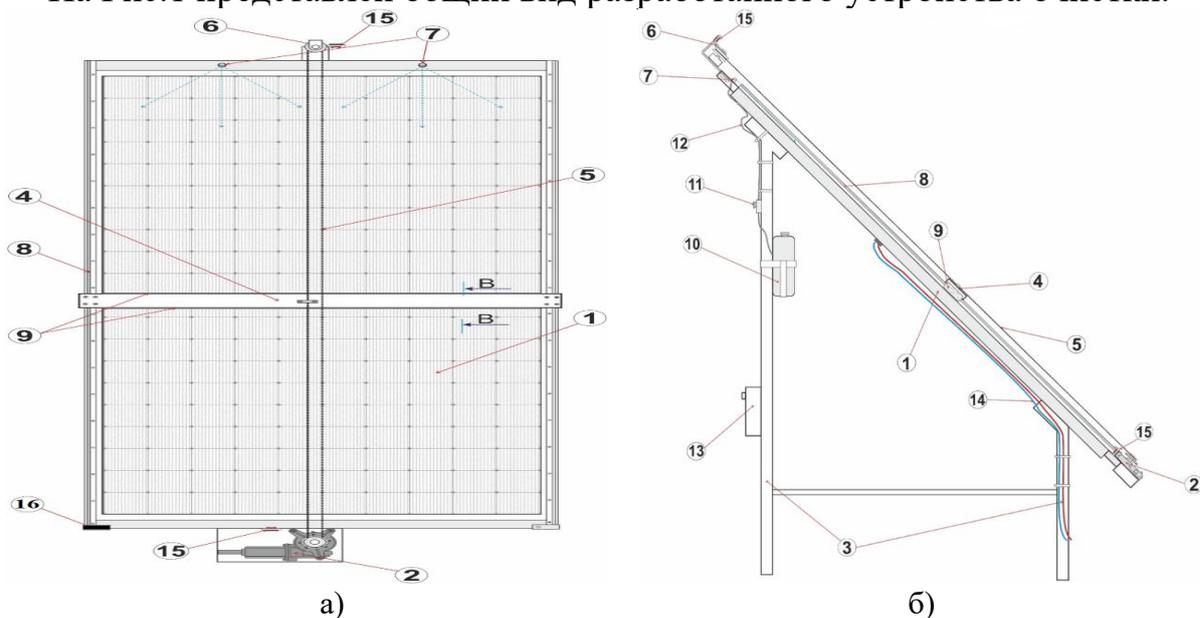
Чертежи устройства очистки: а – вид спереди; б – вид сбоку
